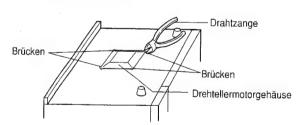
(a). Ausbau des Drehtellermotorgehäuses
